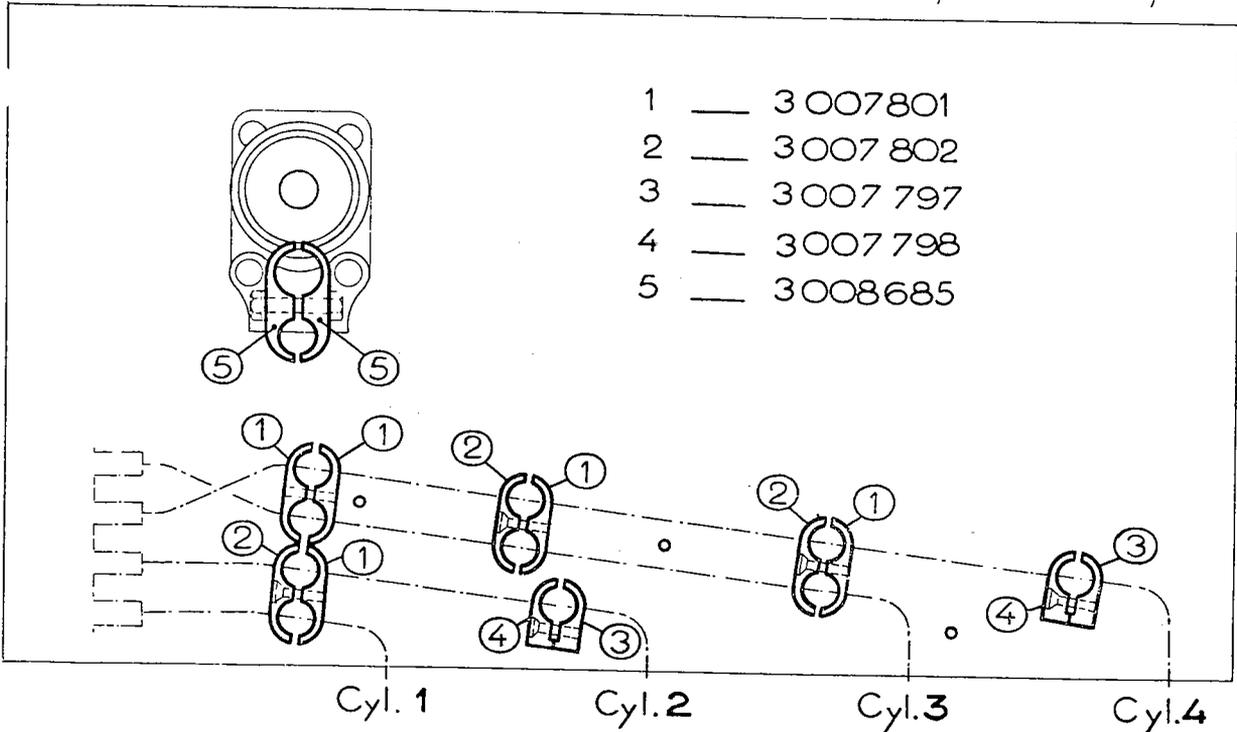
MONTAGE DES TUBES DE DÉMARRAGE
